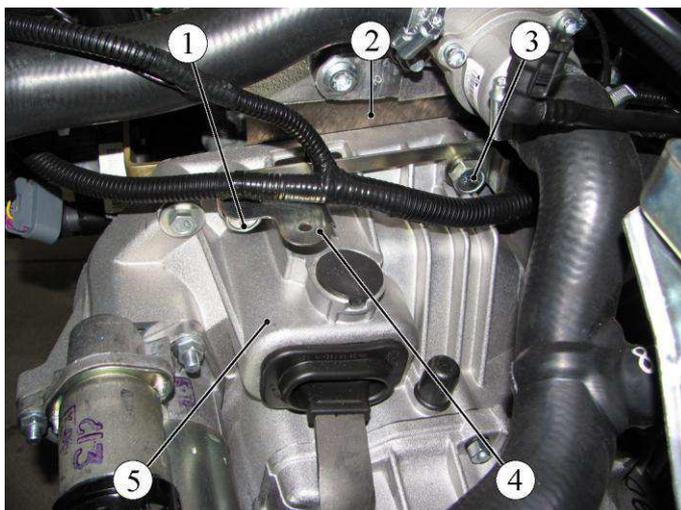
Отсоединение коробки передач от двигателя:
